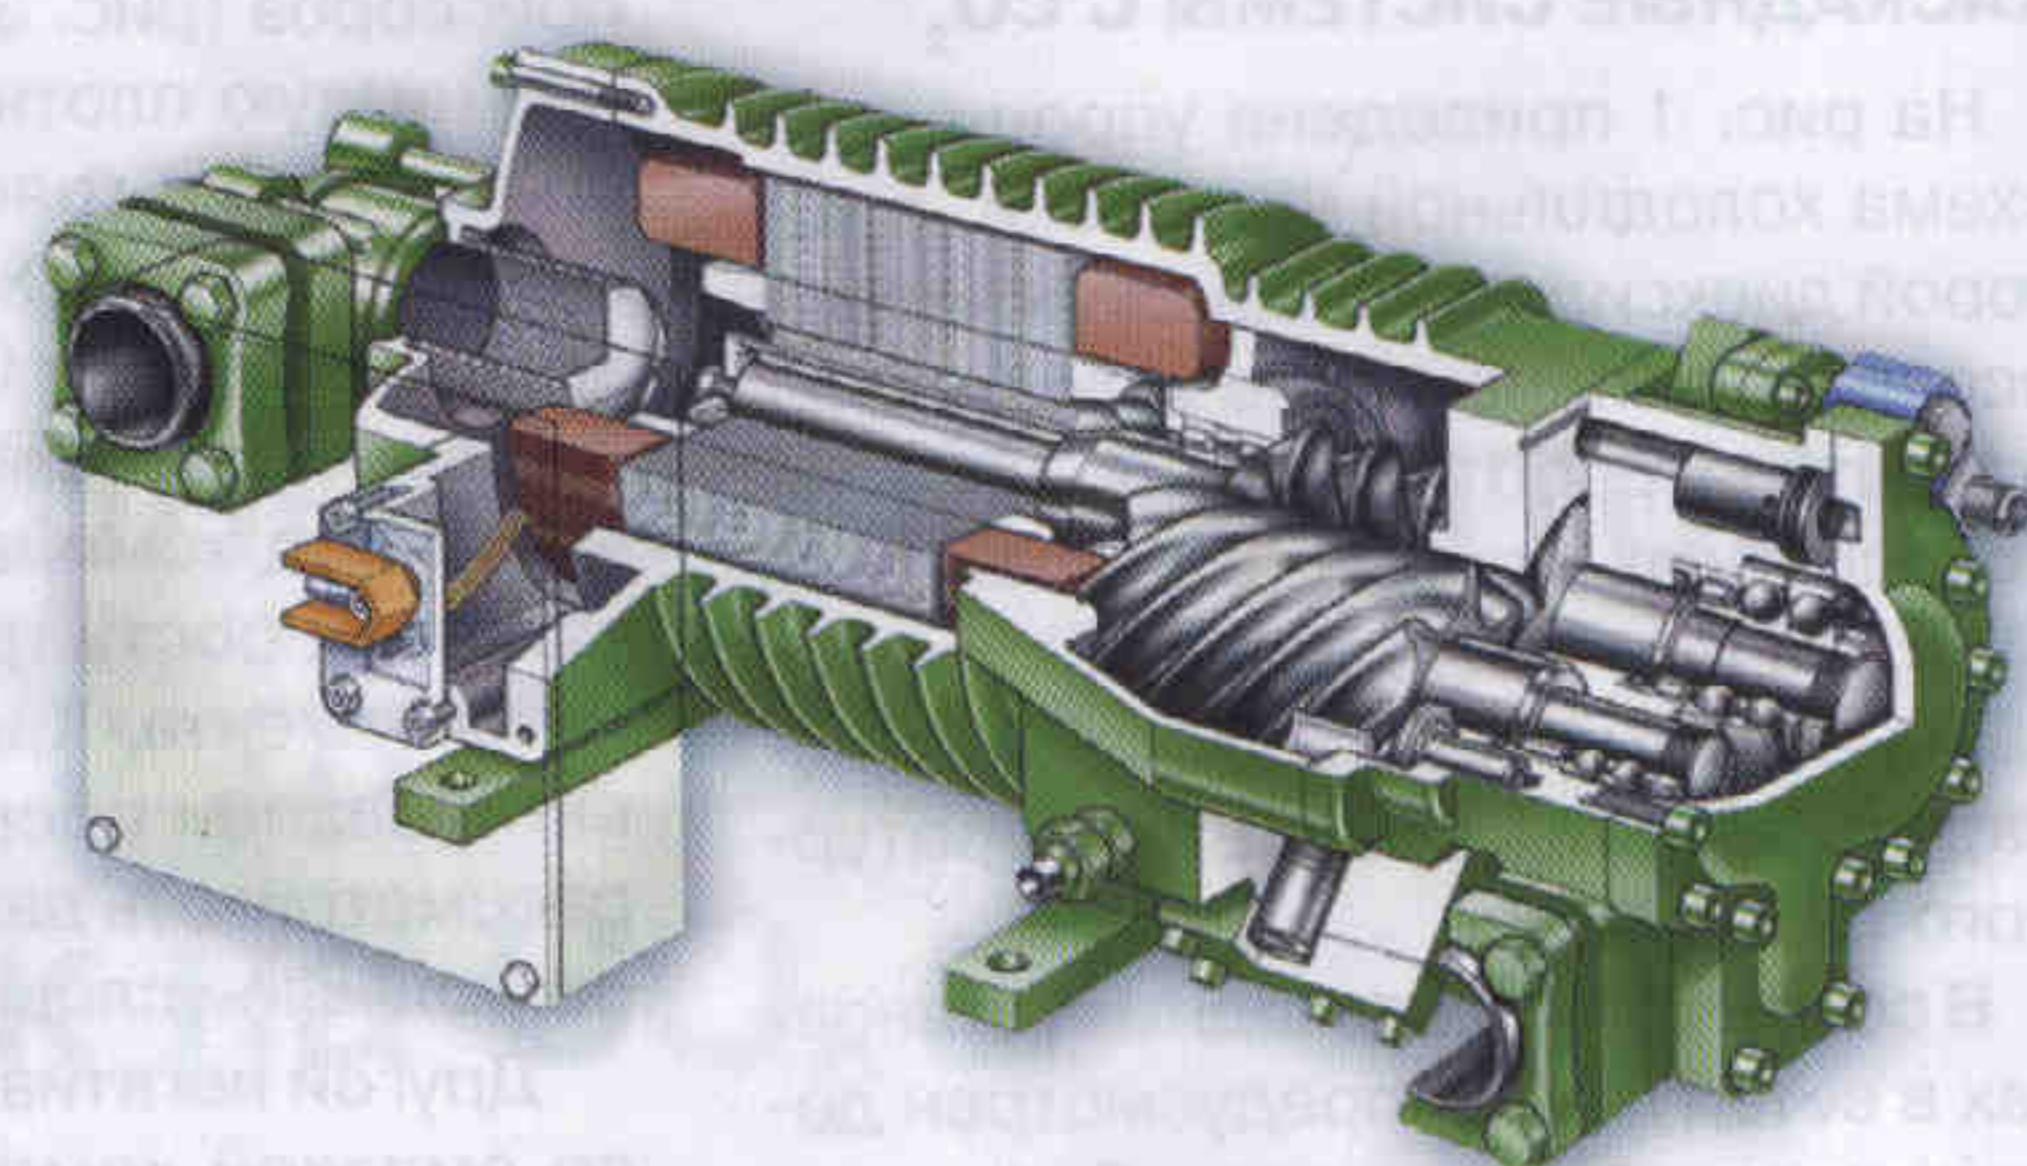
Разрез полугерметичного винтового компрессора (без маслоотделителя)
